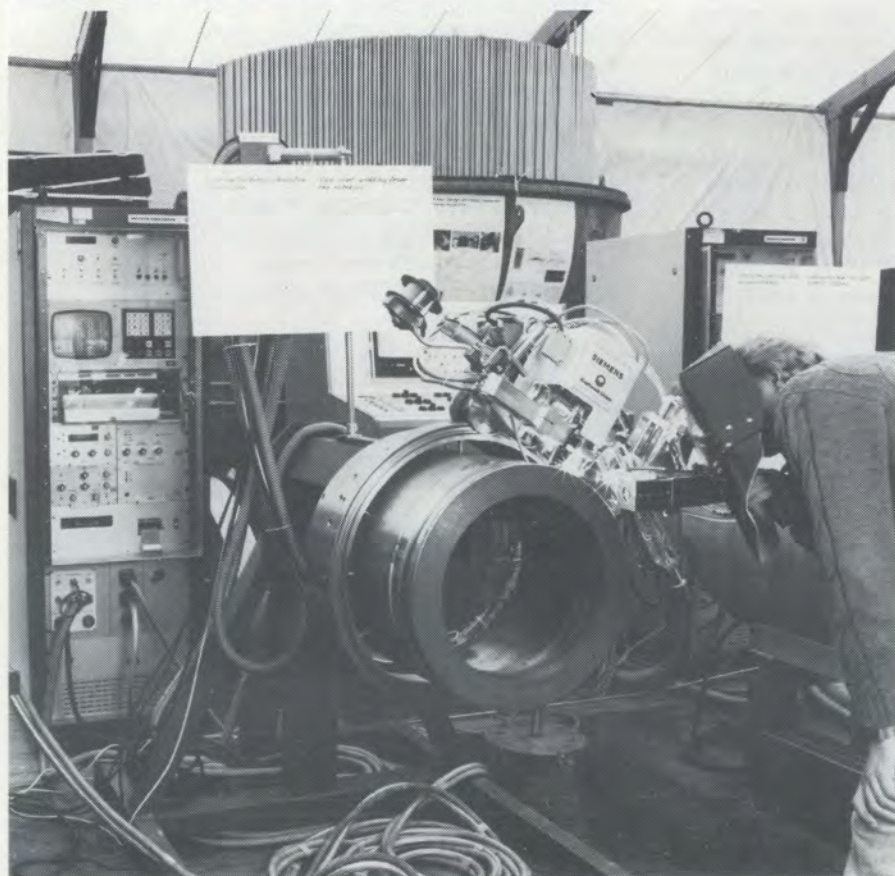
Дистанционно управляемая сварочная машина для сваривания труб
